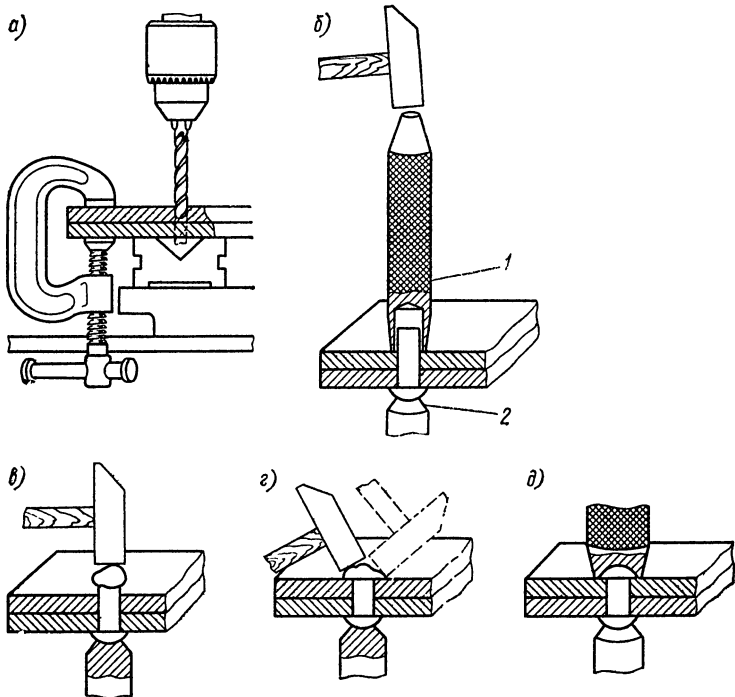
Схема ручной клепки: а — сверление отверстий под заклепки; б — натяжка листов; в — осадка стержня; г — расклепывание замыкающей головки; д — отделка головки
